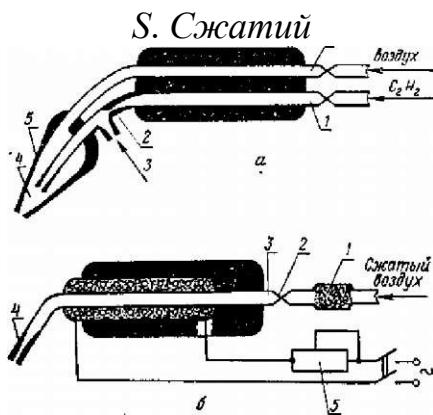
Схема горелок для сварки термопластов горячими газами:
